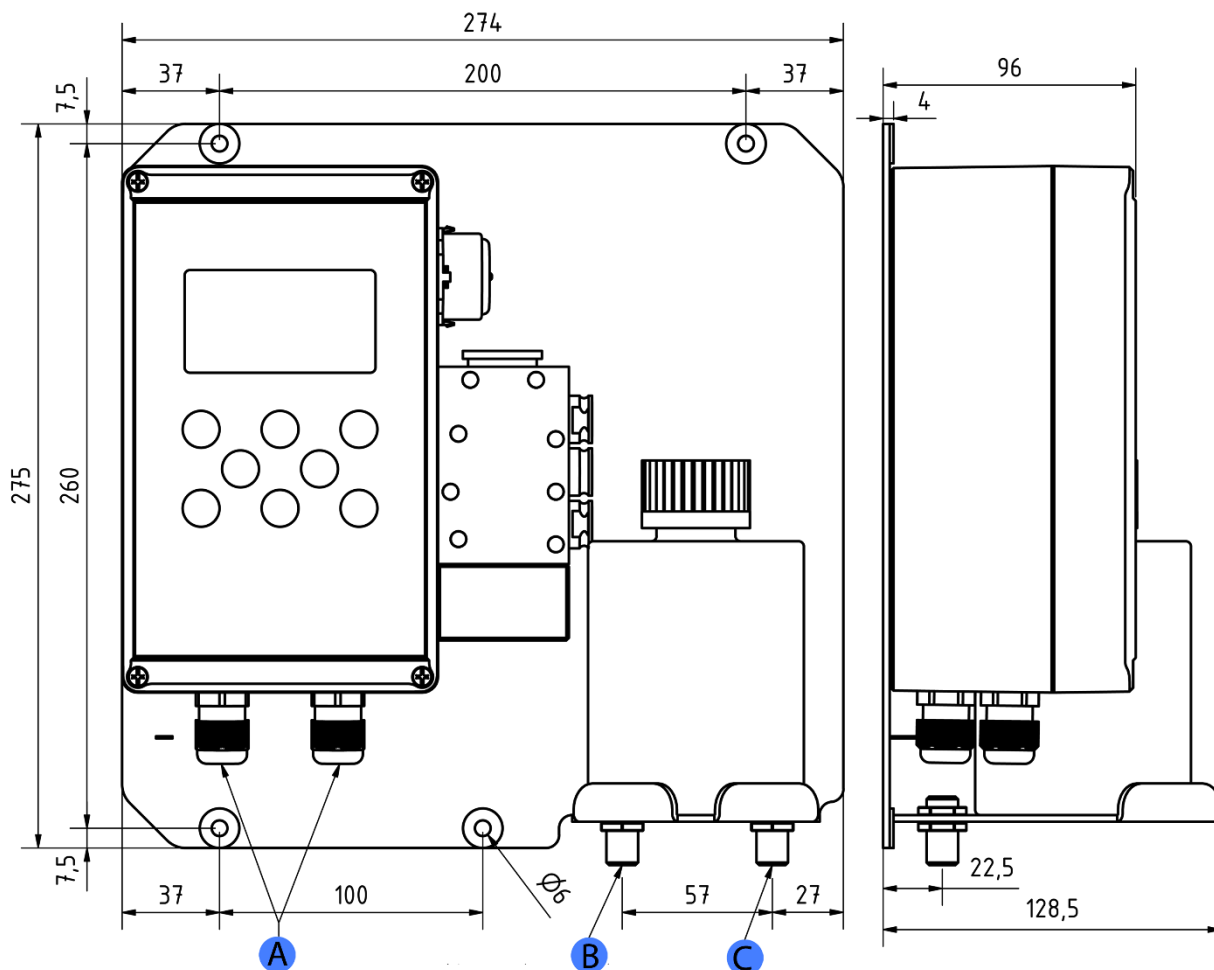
Bohrplan zur Befestigung des Analysegerätes ohne Gehäuse
